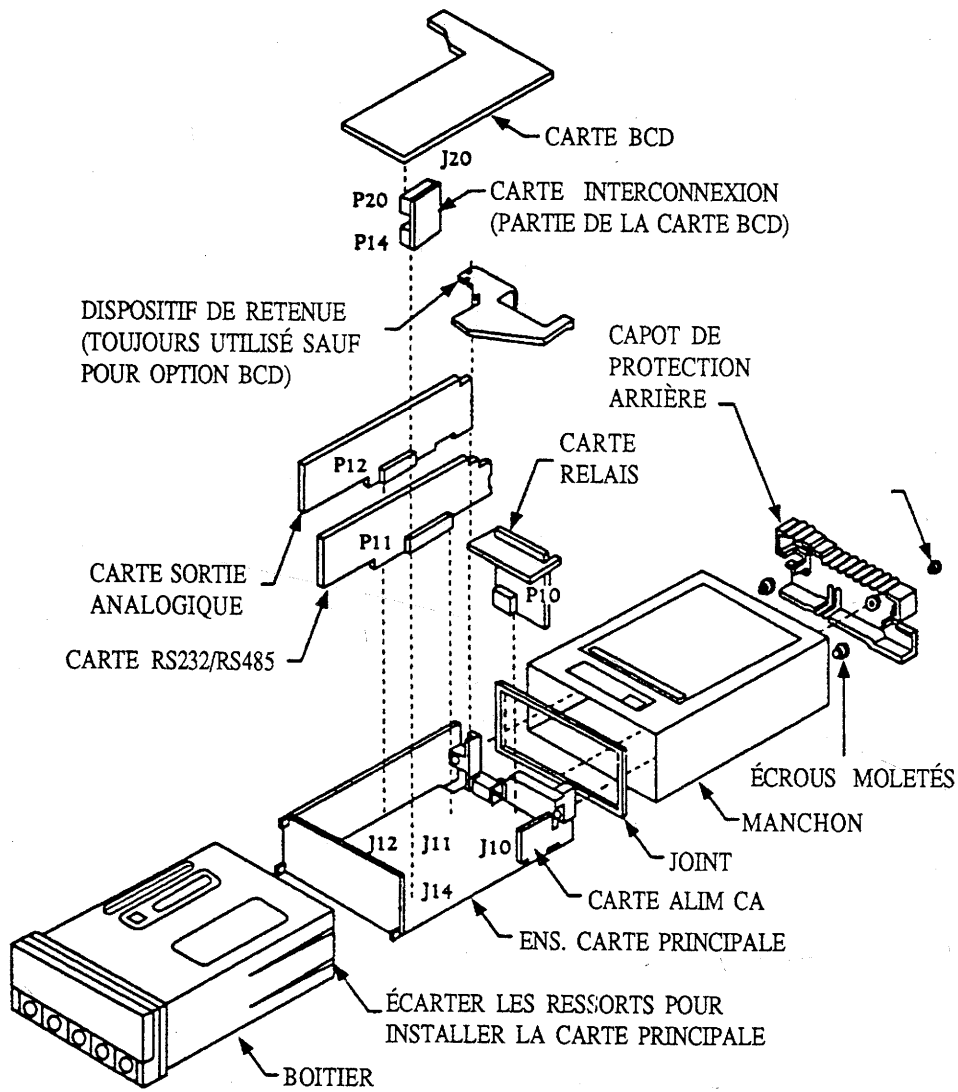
Vue éclatée de la carte principale et des cartes en option
